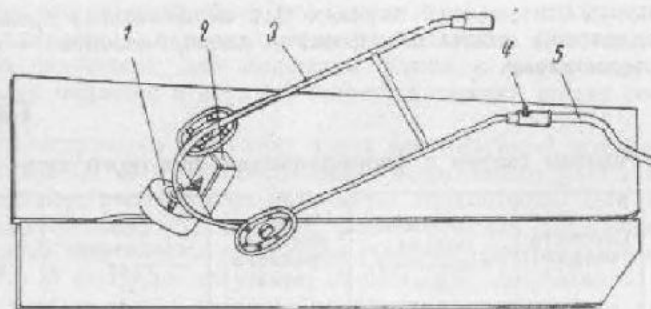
Сборочно-сварочный прижим на тележке.
